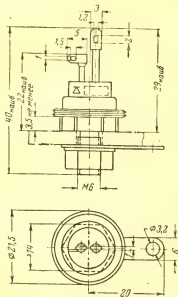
Габаритный чертеж диодов Д235А—Д235Г.
